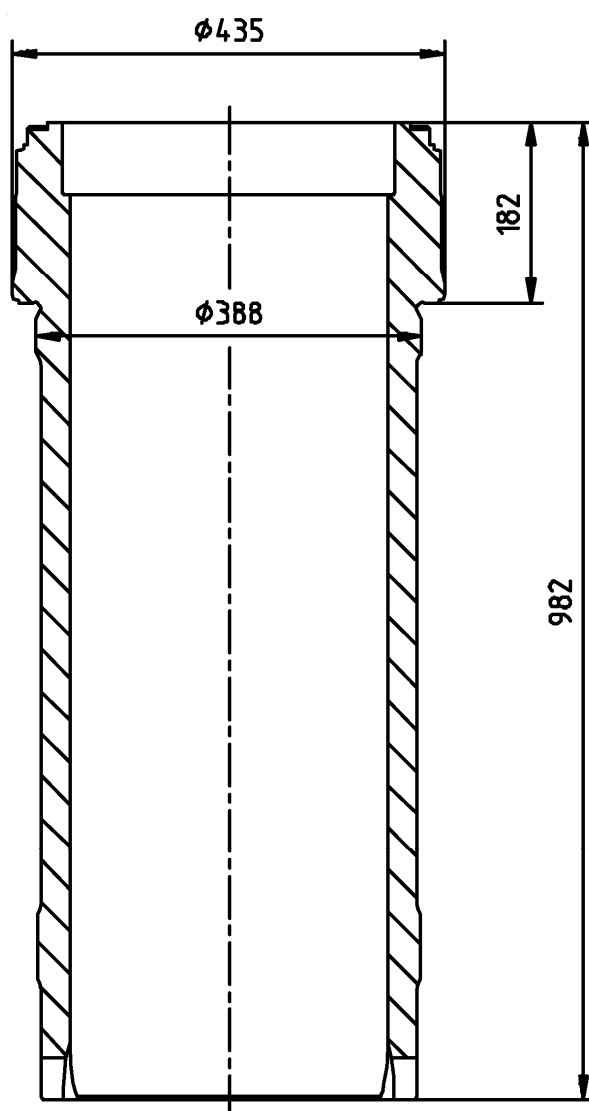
Втулка циліндра двигуна МаК М32С
